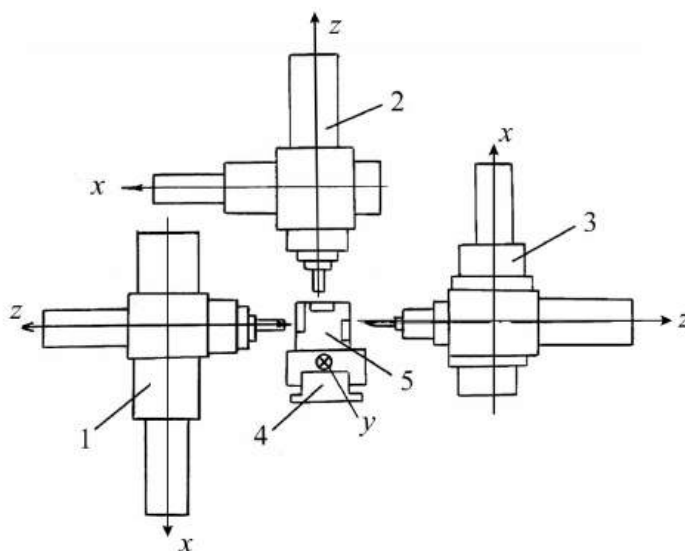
Трьохсторонній операційний фрезерний модуль
